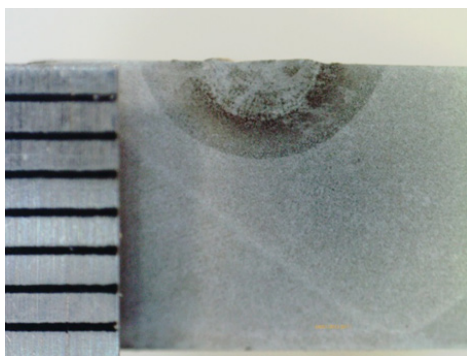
Поперечные разрезы зоны сварного шва после обработки FB-TIG:
